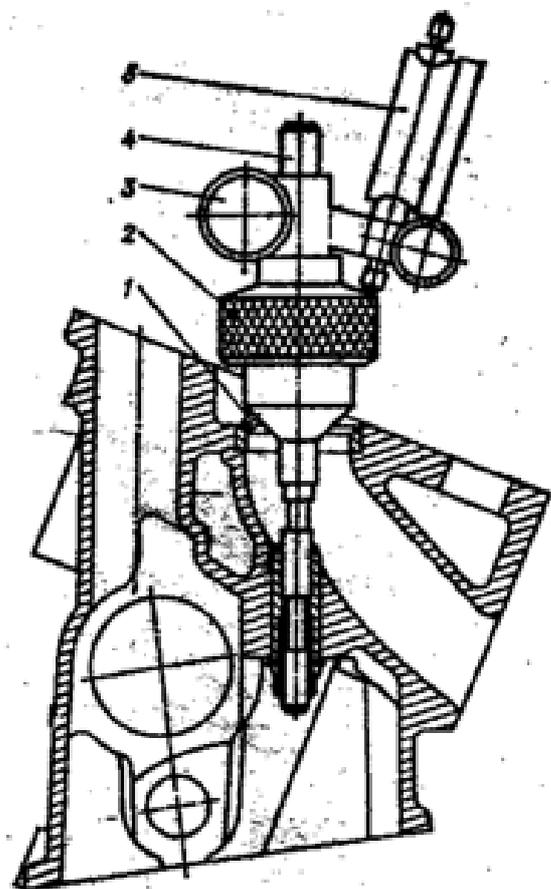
Приспособление для проверки concentричности фаски седла клапана и оси направляющей втулки: 1 - шариковая головка; 2 - вращающаяся муфта; 3 - держатель; 4 - оправка; 5 - индикаторная головка
